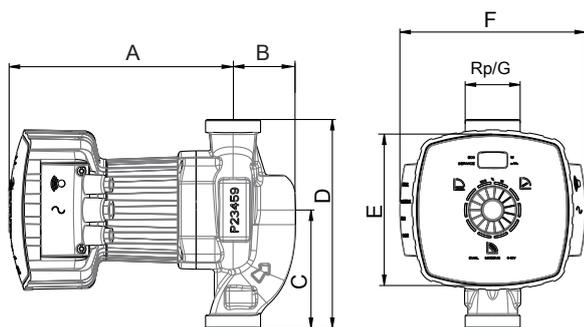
Pumpenaggregat mit Gewindeanschluss
